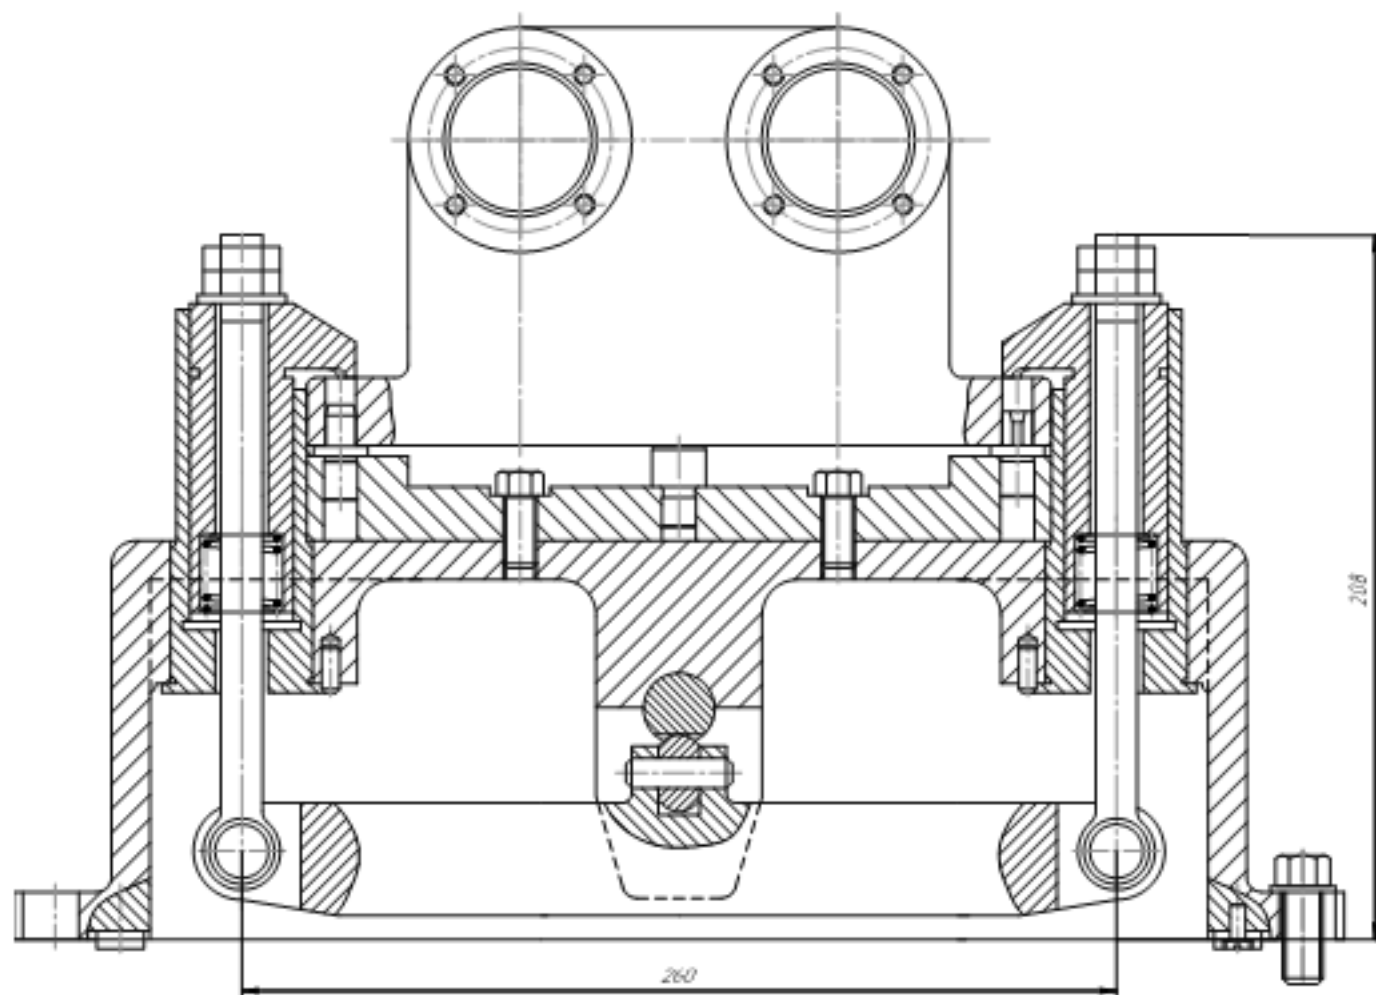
Конструктивна схема верстатного пристосування
